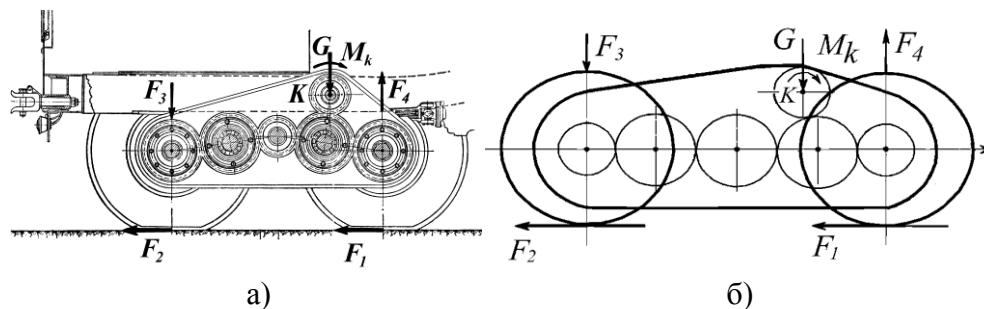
Несимметричный блокированный балансирующий колесный движитель (а) и его схема (б)
